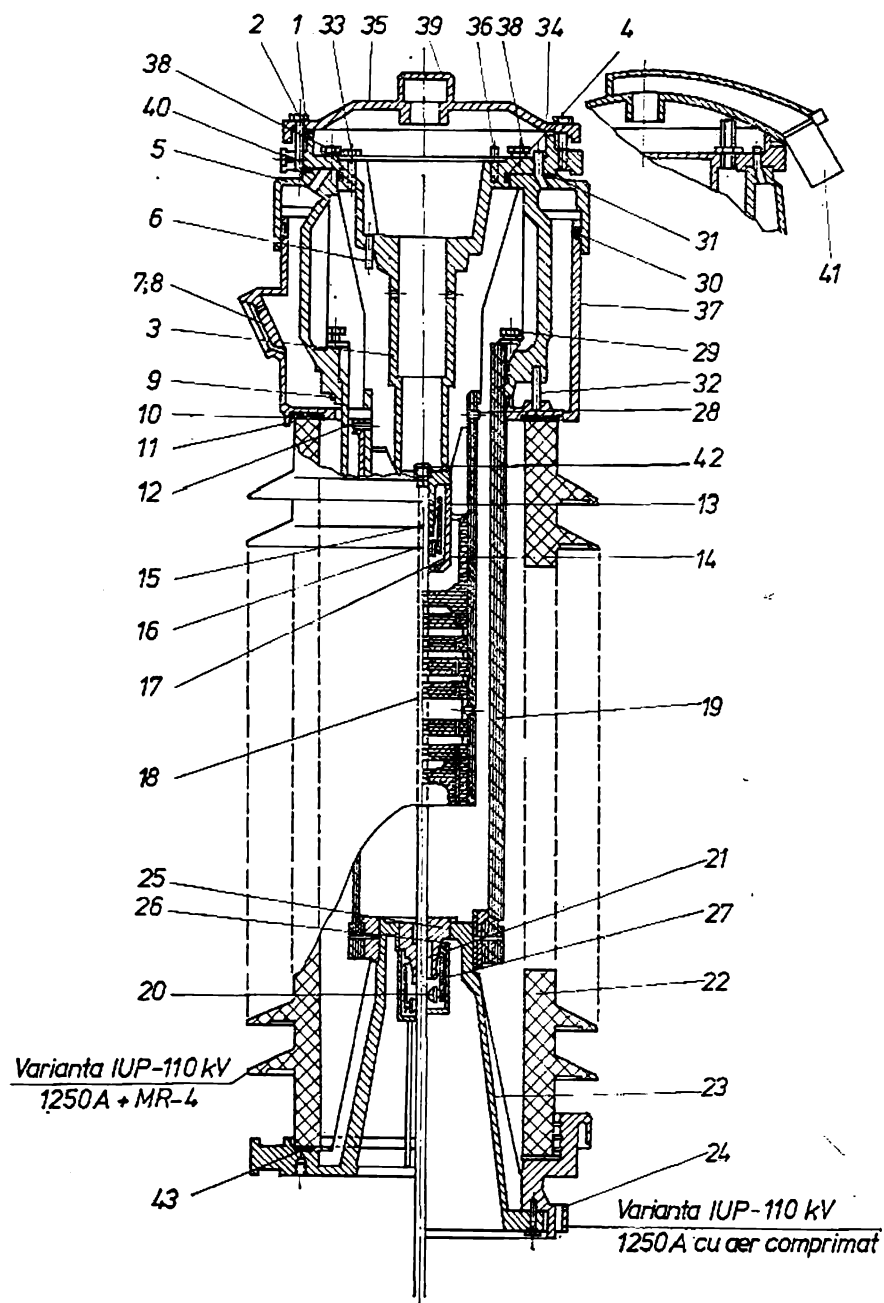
Înteruptoare IUP-110. Secțiune prin ansamblu cameră de stingere :
